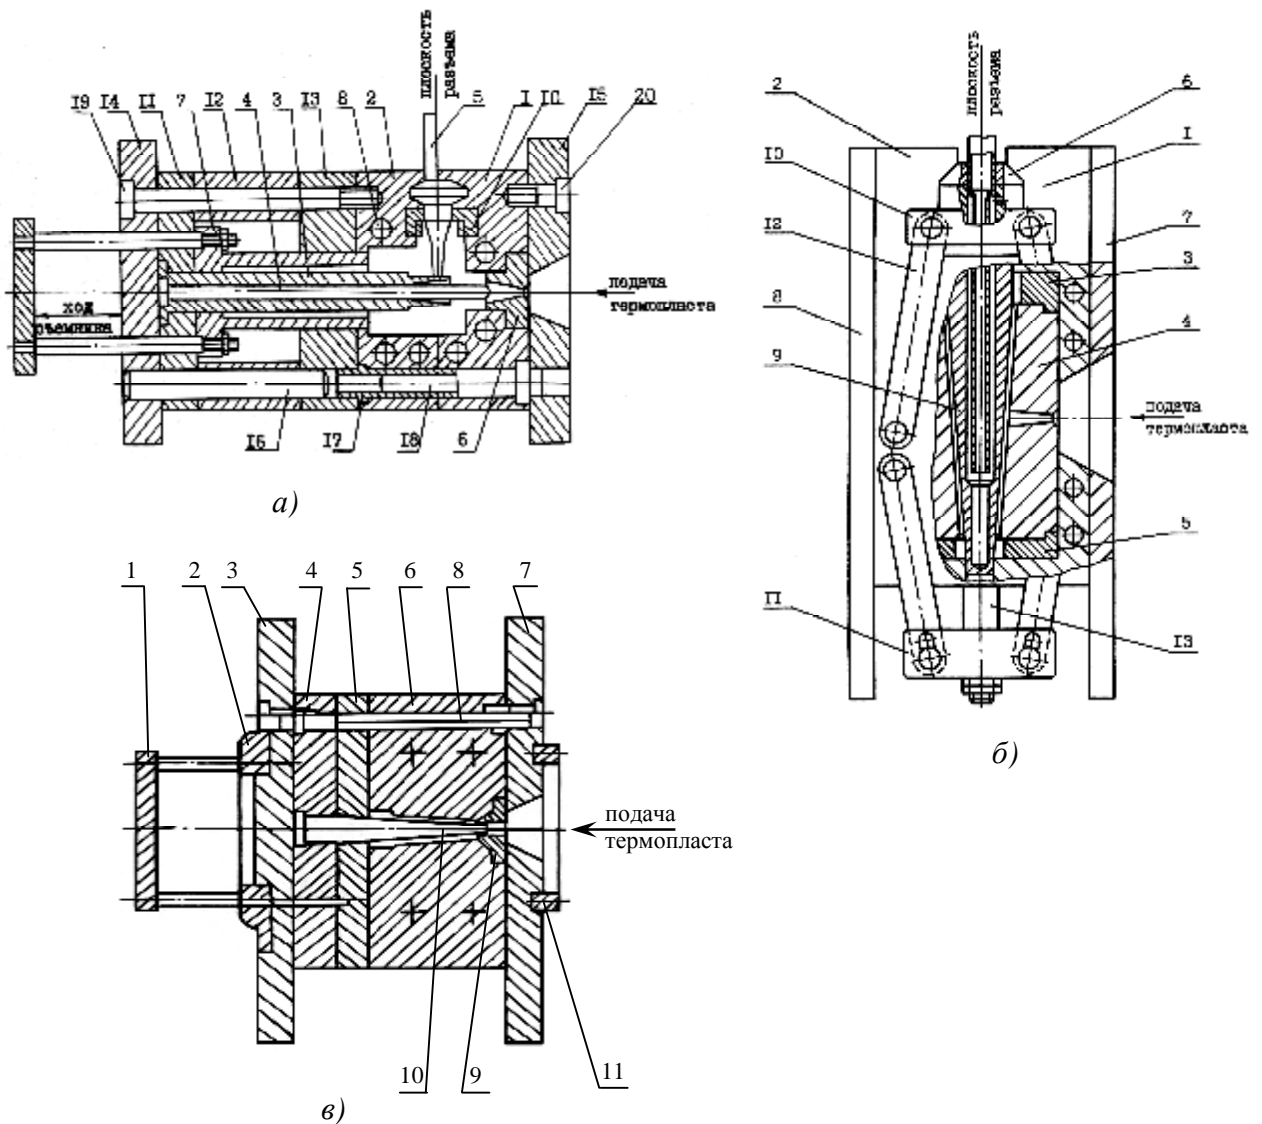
Литьевые формы для изготовления деталей гидроциклона:
